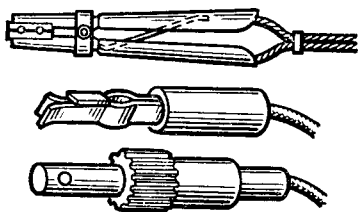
Электрододержатели для ручной дуговой сварки
